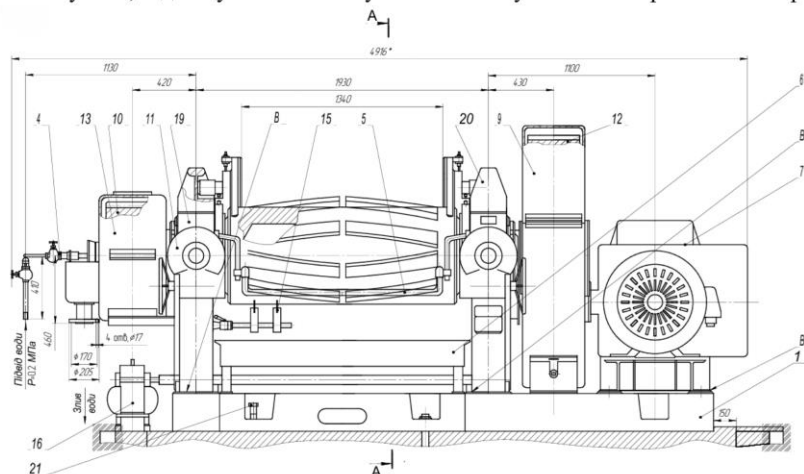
Загальний вигляд модернізованих вальців: 1 – станина; 4 – клапан; 5 – траверса; 6 – штанга аварійних вимикачів; 7 – вузол ножів; 9 – трубопровід; 11 – змащування підшипників; 12 – механізм контролювання зазору; 13 – редуктор приводу вальців; 15 – фрикційна шестерня; 16 – зливний клапан; 19 – вузол зливу води; 20 – кінцевий вимикач; 21 – болти регулювання
